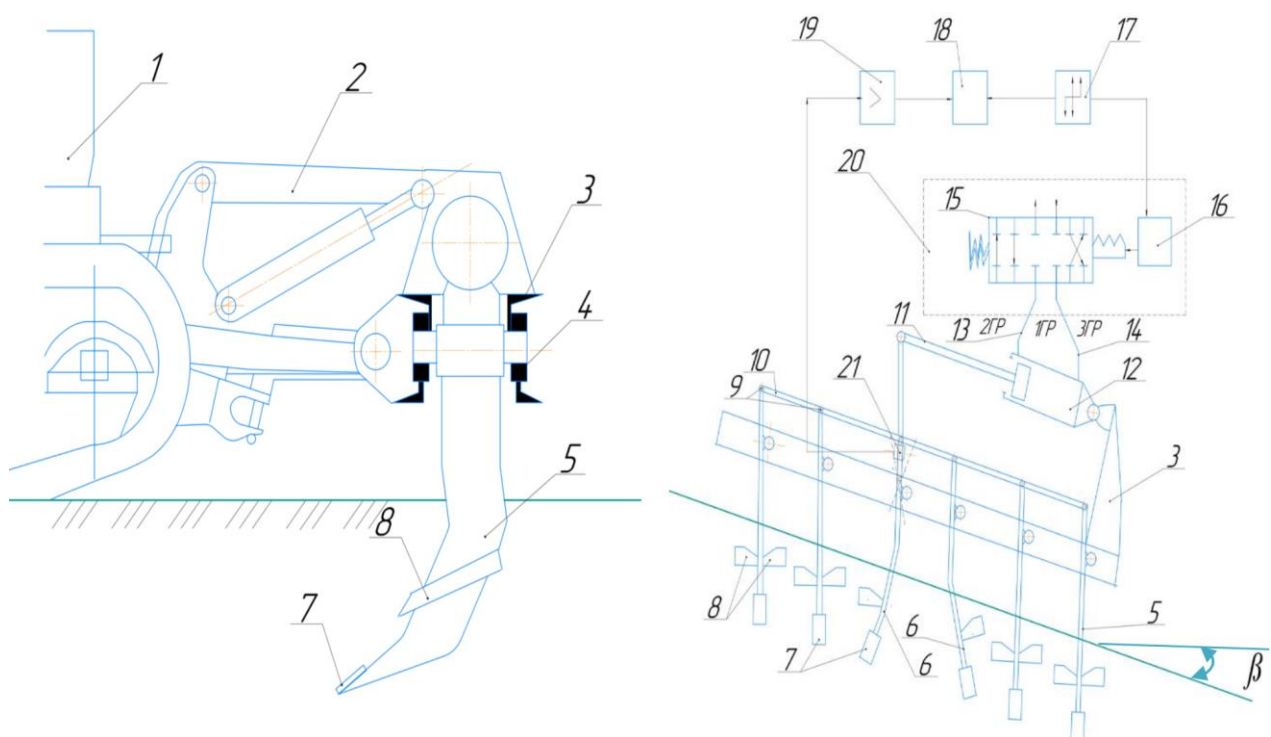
Конструктивна схема розробленого глибокорозпушувача.
